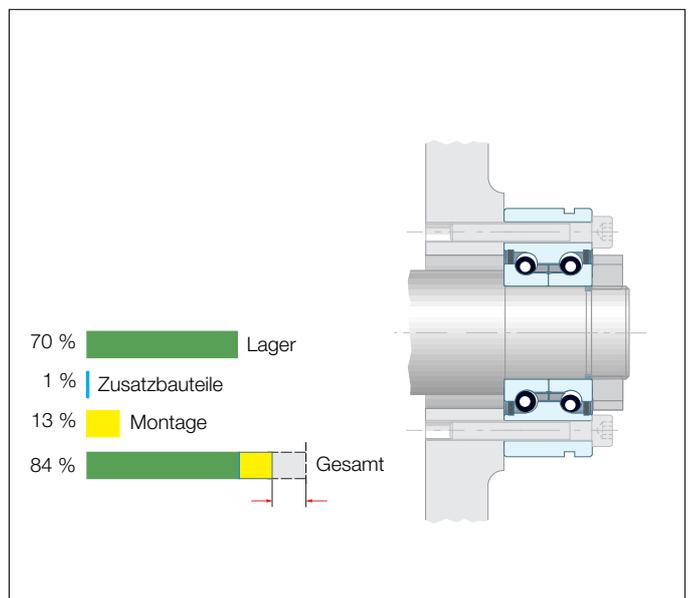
Einsparungspotenzial einer Lagerlösung mit einem plan angeschraubten Lager ZKLF
